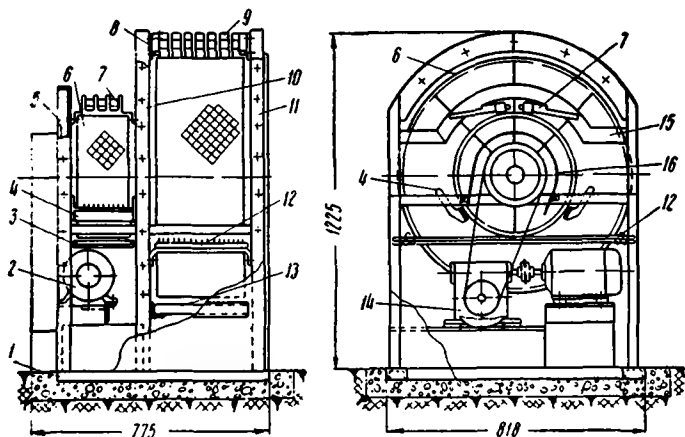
Приспособление для предварительной притирки щеток тягового двигателя ЭДТ-200 и генератора МПТ-99/47:
